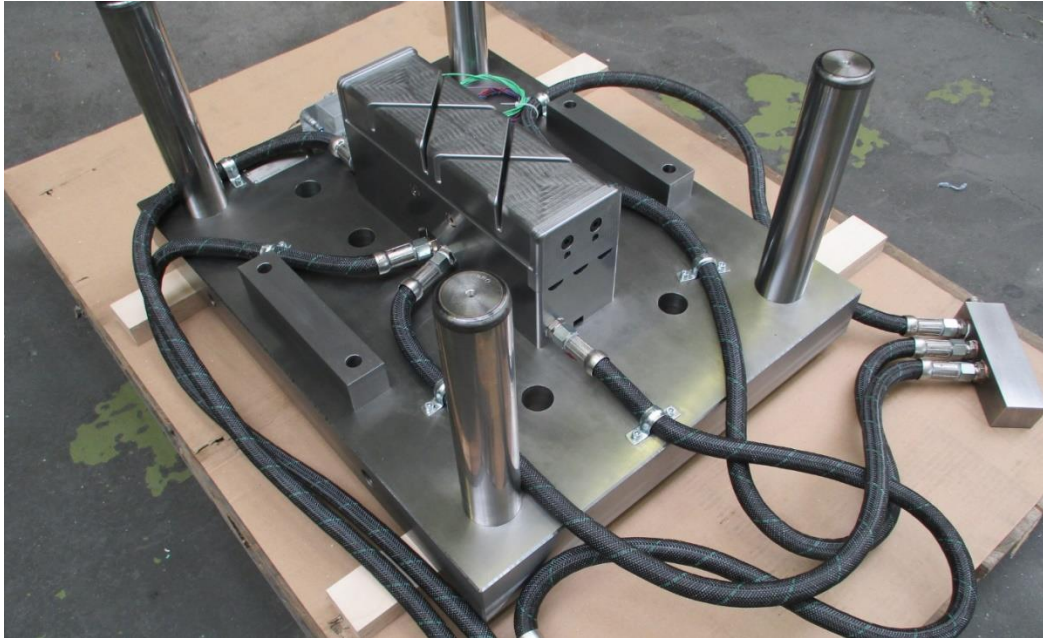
Werkzeug-Unterteil Versuchswerkzeug 1 gen. Testkörper
